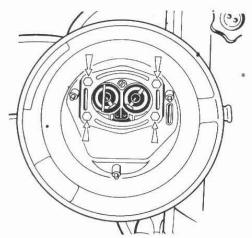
Desmontaje del filtro de aire. Con las flechas se indican las tuercas de sujeción del cuerpo del filtro al carburador
